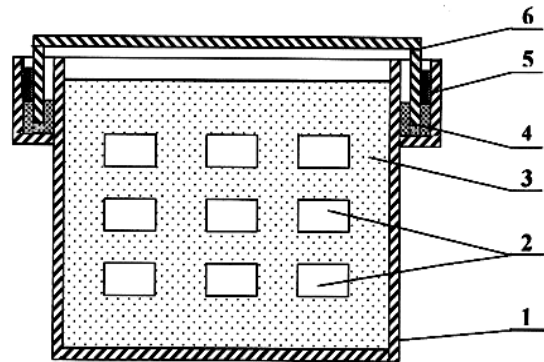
Схема диффузионного борирования: 1 – корпус контейнера; 2 – образцы или детали; 3 – рабочая порошковая смесь; 4 – отработанная порошковая смесь; 5 – силикатная крошка (плавкий затвор); 6 – крышка контейнера
